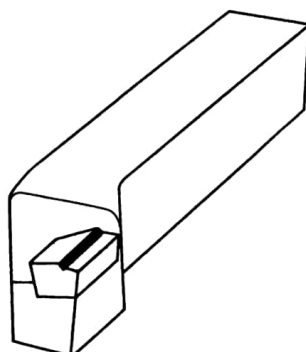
Meißel mit eingeschliffener Spanleitstufe
